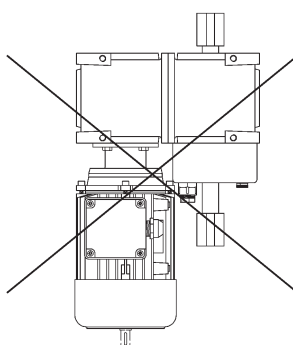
Forskellige montagemuligheder. Gearet er set fra siden.
